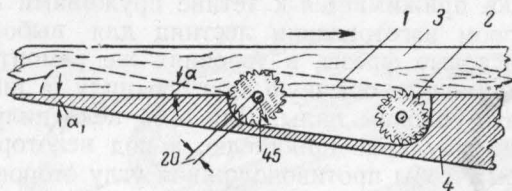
Линейка для фрезеровки пазов в тетиве лестницы-палки:
